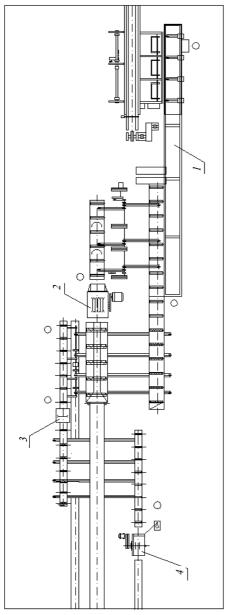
Схема цеха на базе вертикального ленточнопильного станка ЛЛК-2: I – ленточнопильный станок; 2 – многопильный круглопильный станок; 3 — торцовочный станок; 4 — фрезерно-обрезной станок
